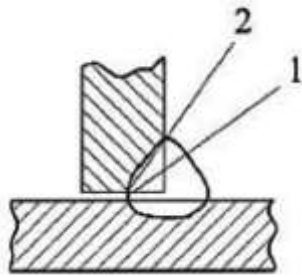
Розрахункові перерізи зварного з'єднання з кутовим швом
